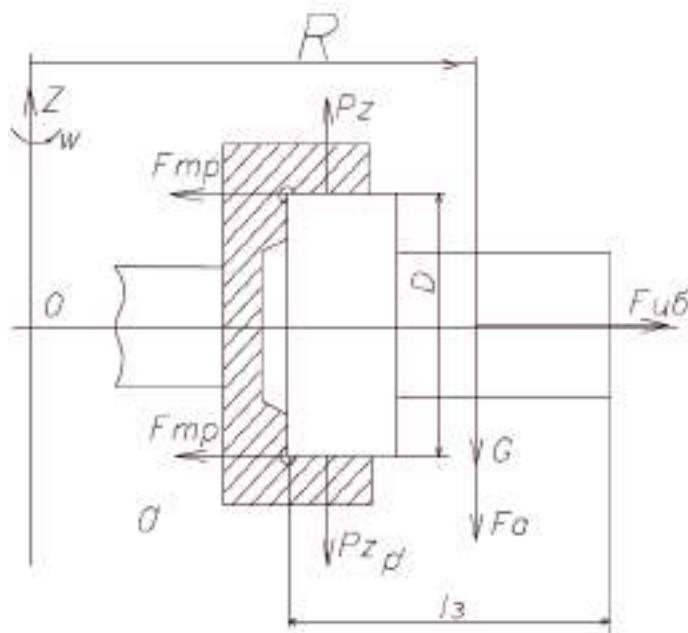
Расчетная схема для определения усилия закрепления заготовки в схвате ПР
